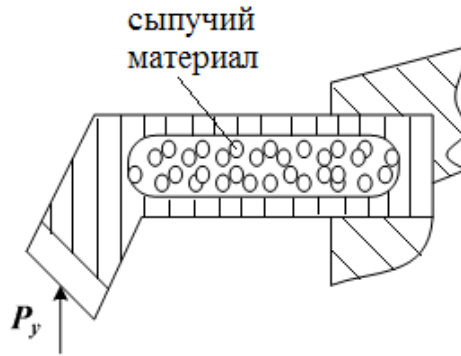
Эскиз сечения расточного резца с сыпучим наполнителем
